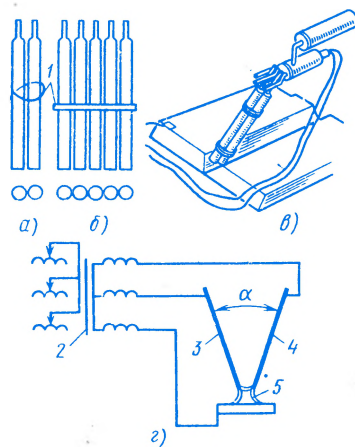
Схема сдвоенного электрода (а), гребенки (б) и сварки трехфазным током (в, г): 1 — связка электродов, 2 — трехфазный трансформатор, 3, 4 — электроды, 5 — дуга
